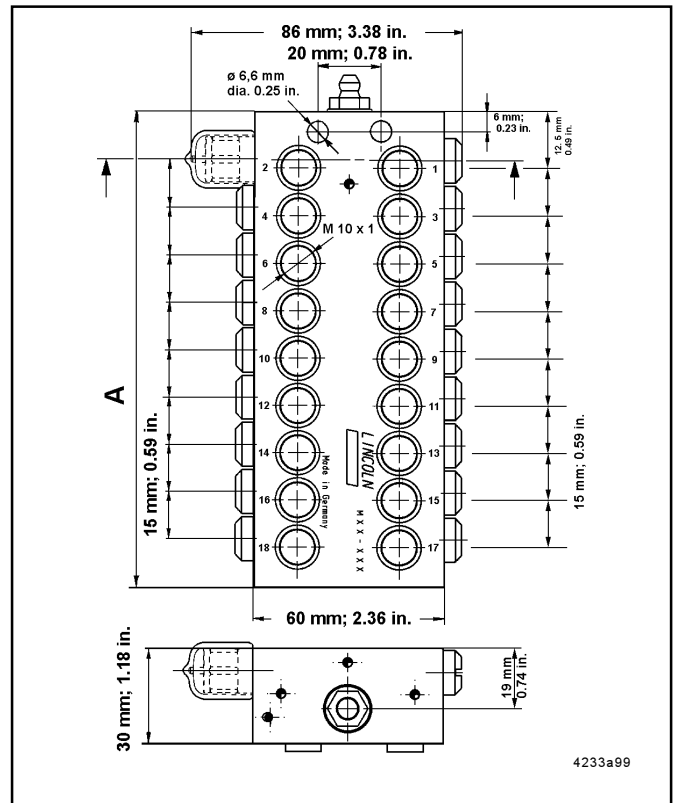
Cotes dimensionnelles du doseur SSV installé à l'arrière
